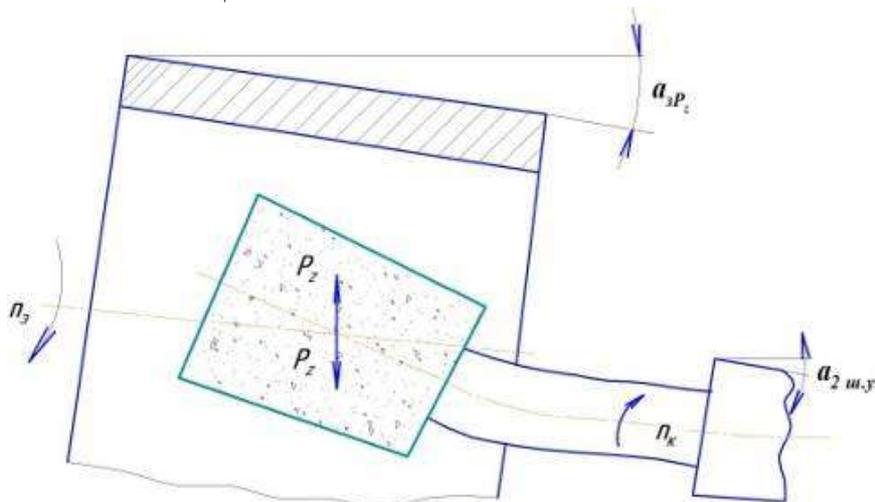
Мгновенное положение конусообразного круга и заготовки под воздействием тангенциальной нагрузки
